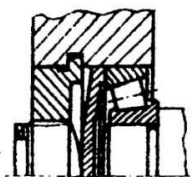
Изменение зазора в подшипнике с помощью регулировочного винта
